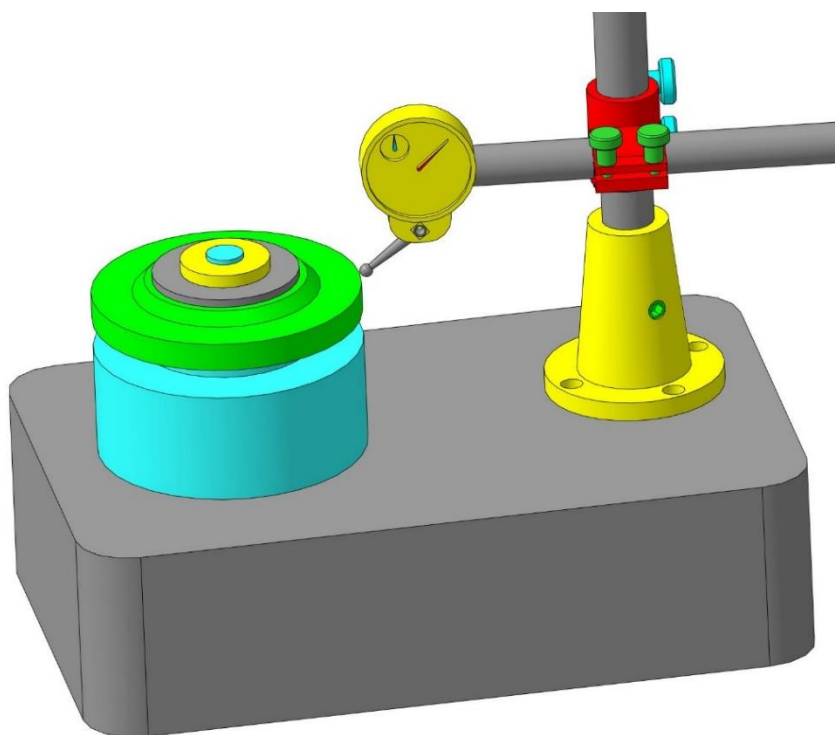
Розроблений контрольний пристрій із деталлю
